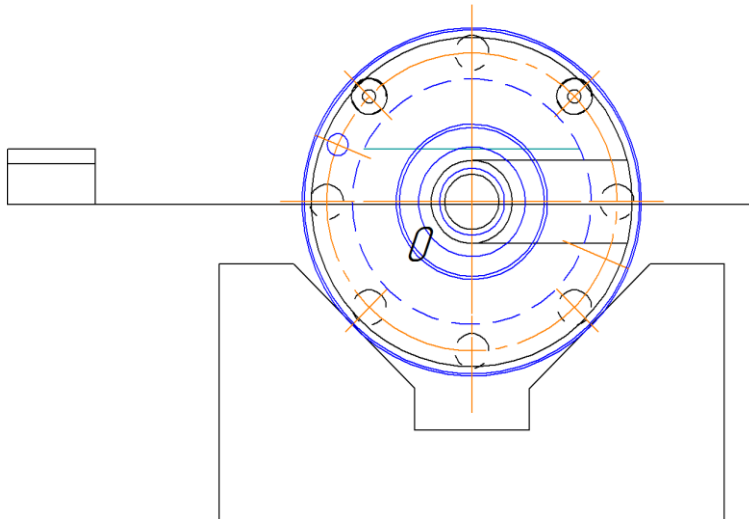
Схема формування розмірів при фрезеруванні нижньої площини в розмір $103,5 \pm 0,1$
